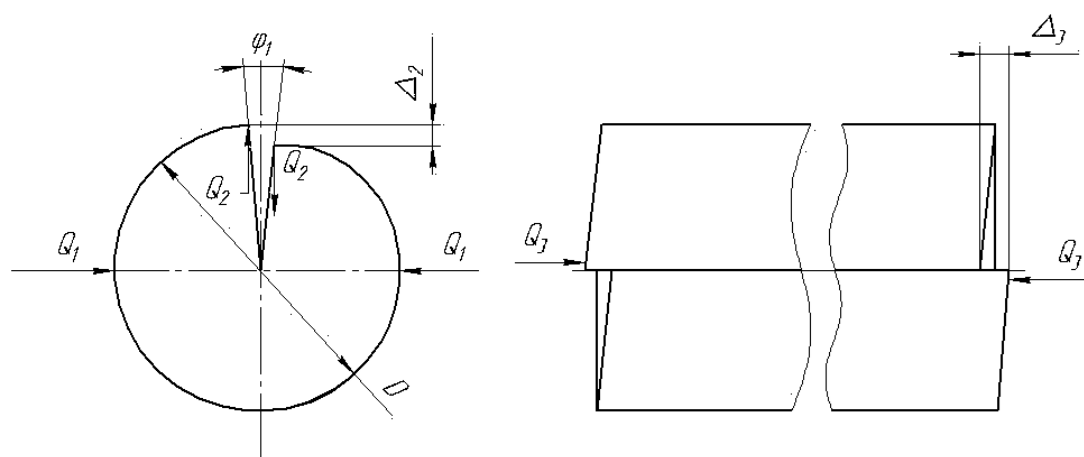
Розрахункова схема довальцювання обичайки [22]
